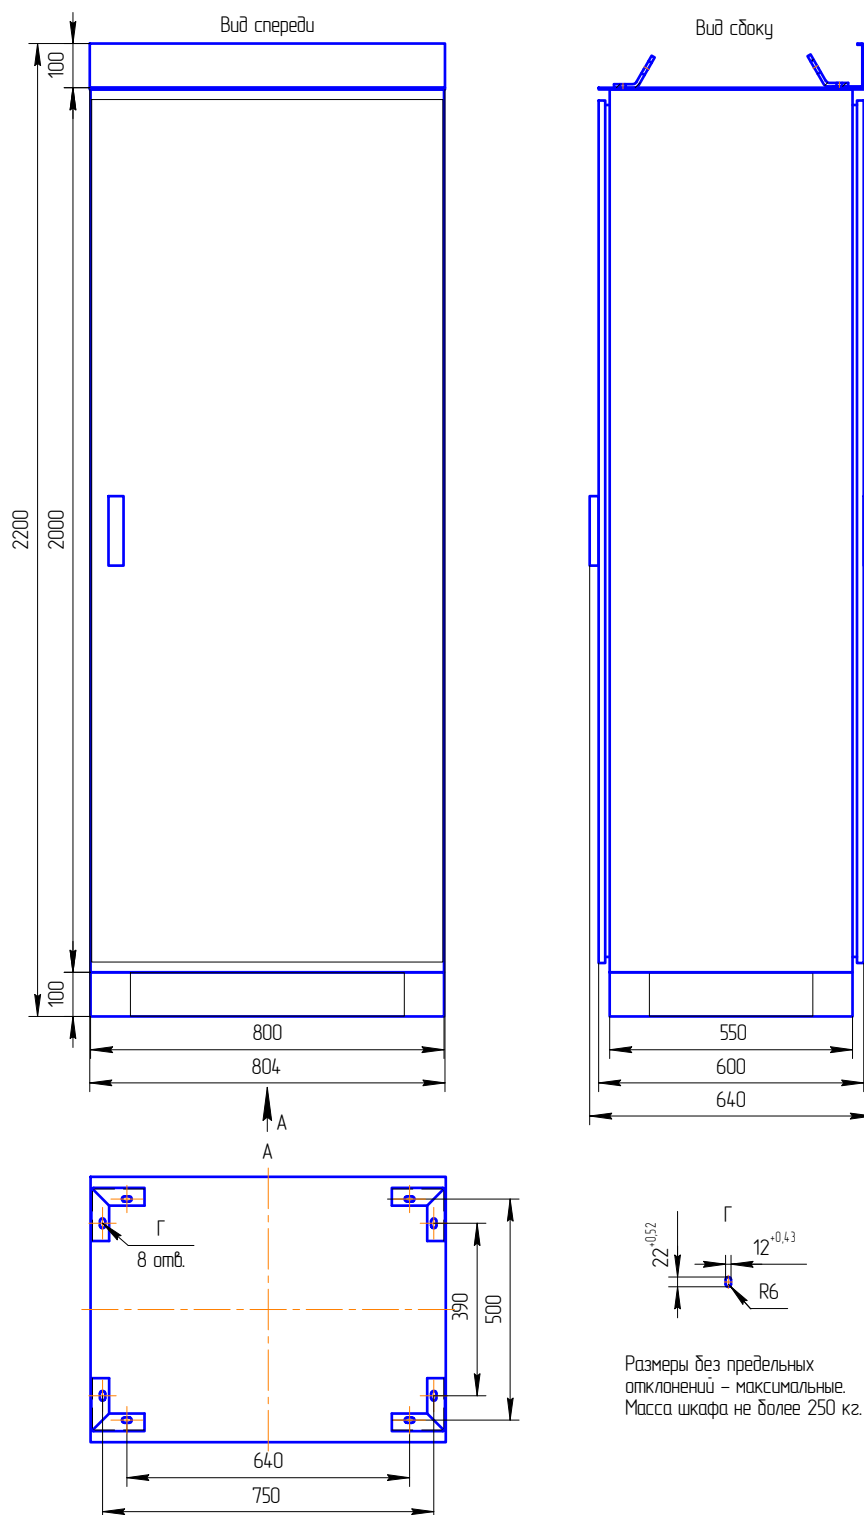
Габаритные и установочные размеры шкафа
